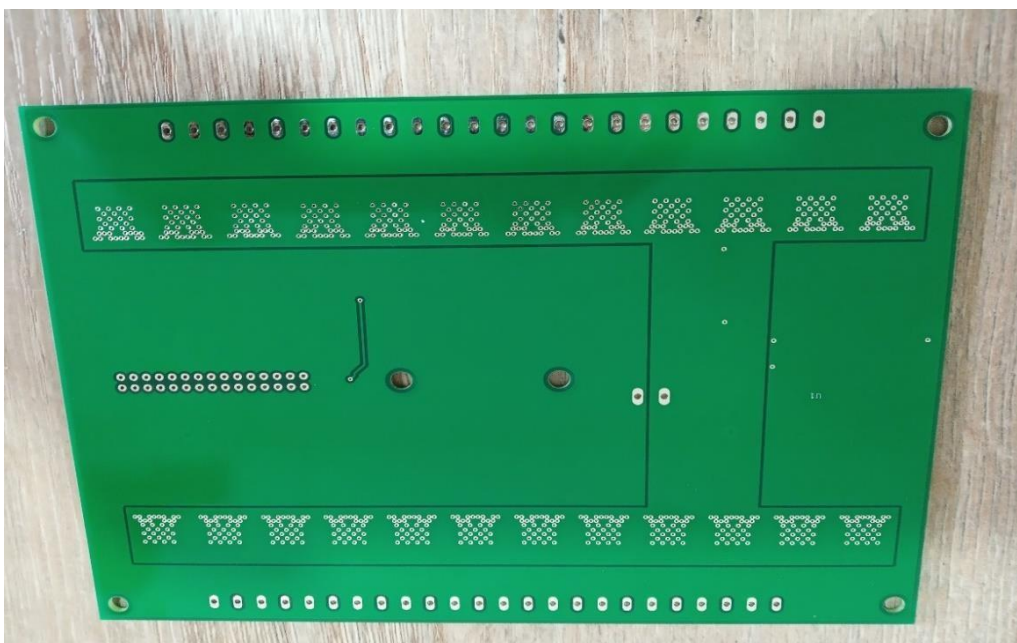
Tarjeta PCB secuenciador de luces AC [Vista inferior]. Tobón. (2019)
